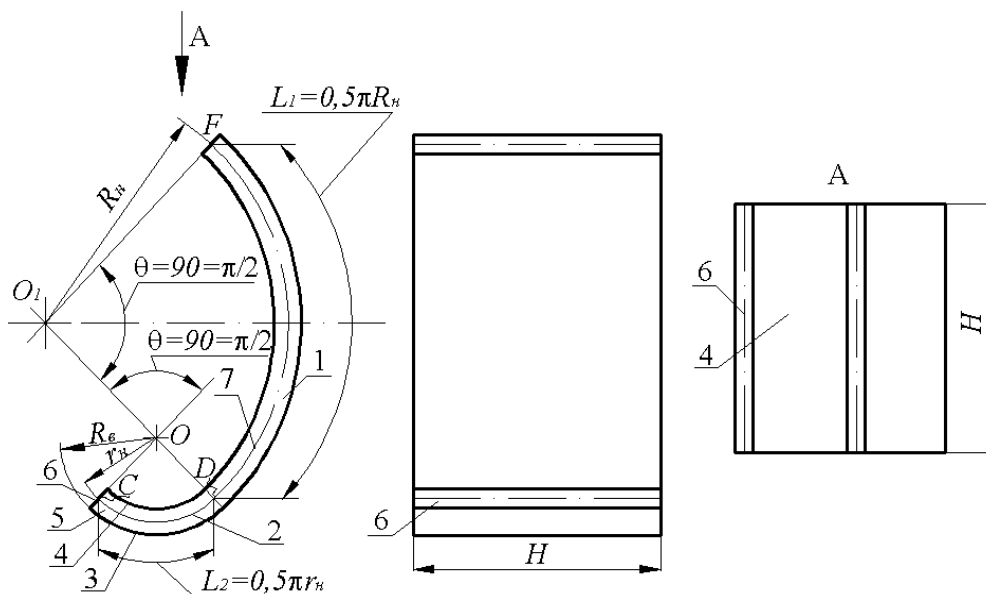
Схематичне зображення удосконаленої конструкції заготовки для згортої втулки
